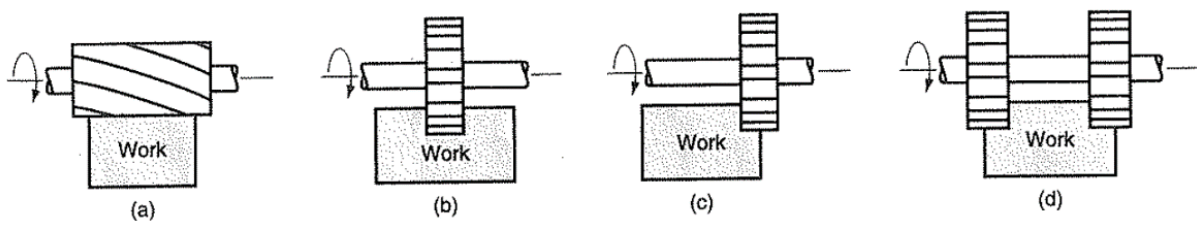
Fresagem periférica: a) faceamento, b) abertura de canal, c) fresagem lateral, e d) fresagem de contorno [22].
